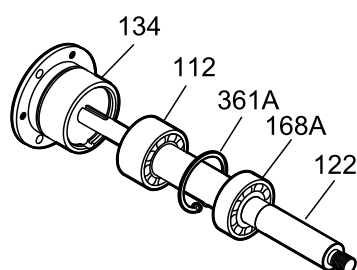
Extracción de la carcasa del rodamiento y de los rodamientos
